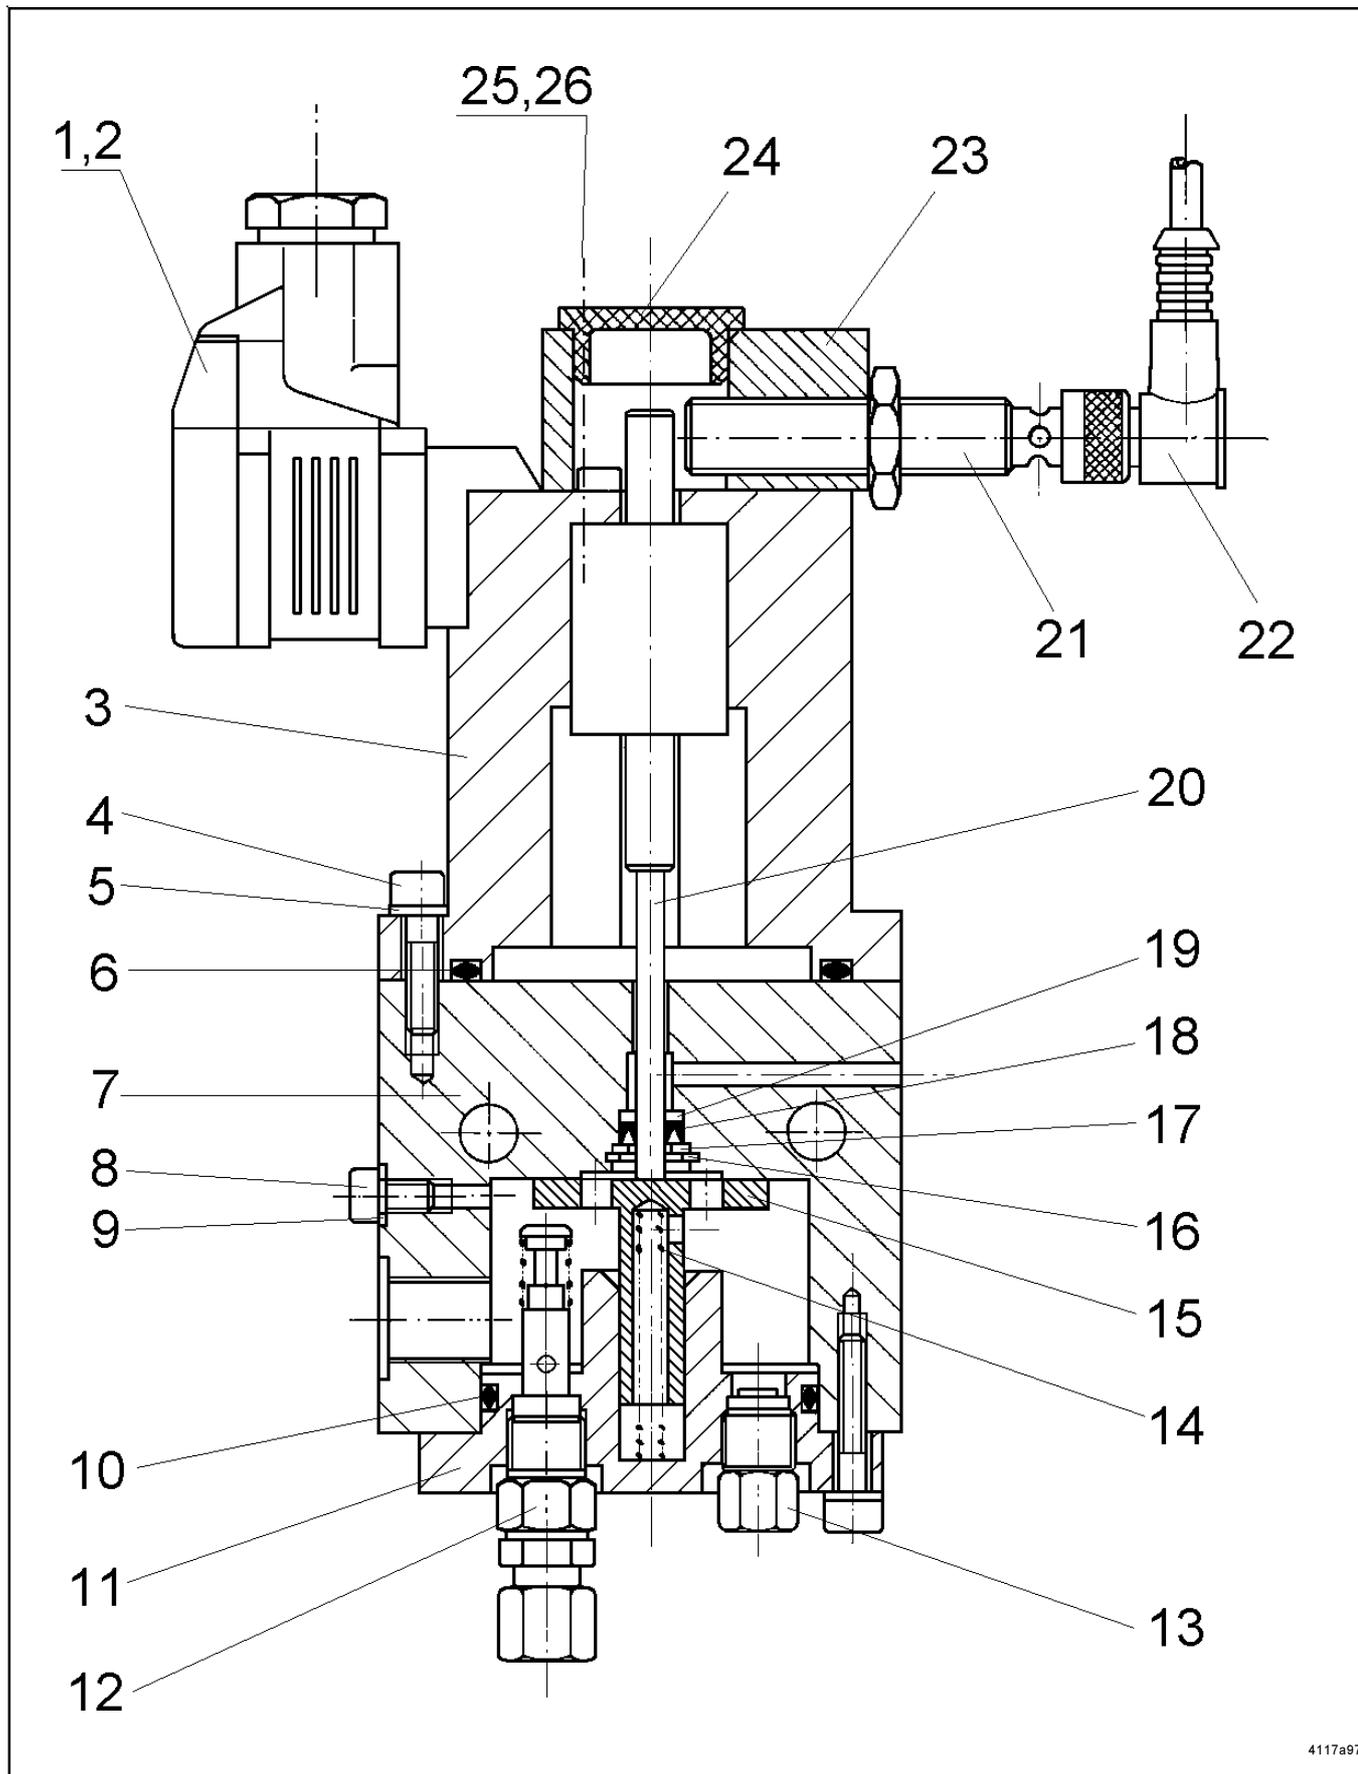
Schnittzeichnung mit Ersatzteilen
